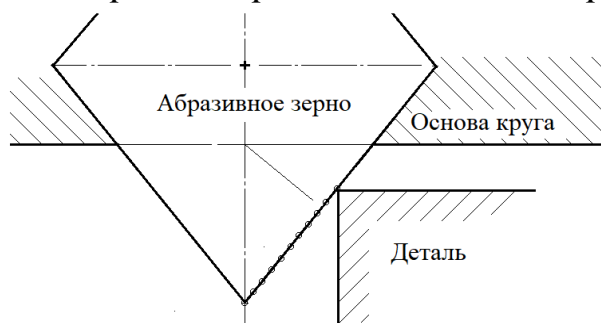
Абразивное зерно и обрабатываемая деталь
